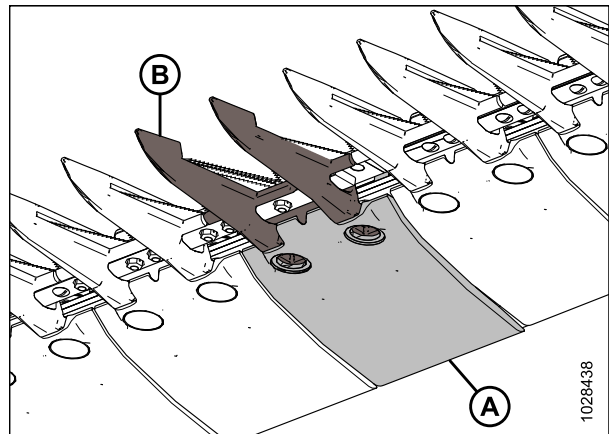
Заостренный центральный противорежущий палец и износная пластина
